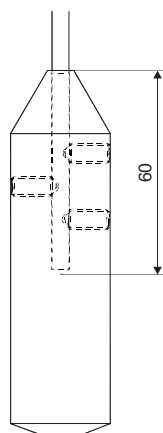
Zobrazení závitového spoje držáku elektrody s tyčovou elektrodou
